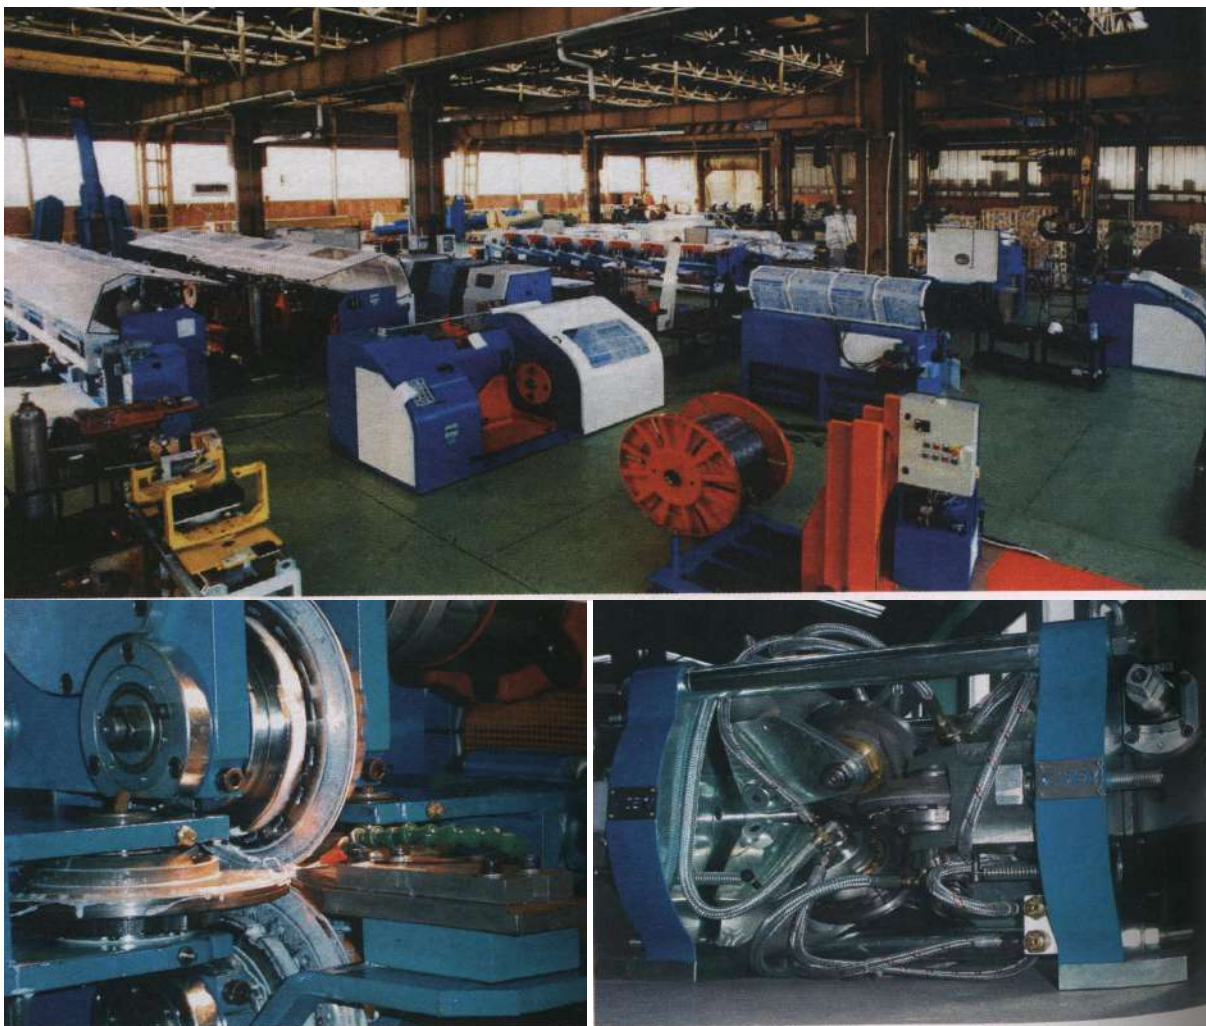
Обладнання для стикового зварювання фірми IDEAL
